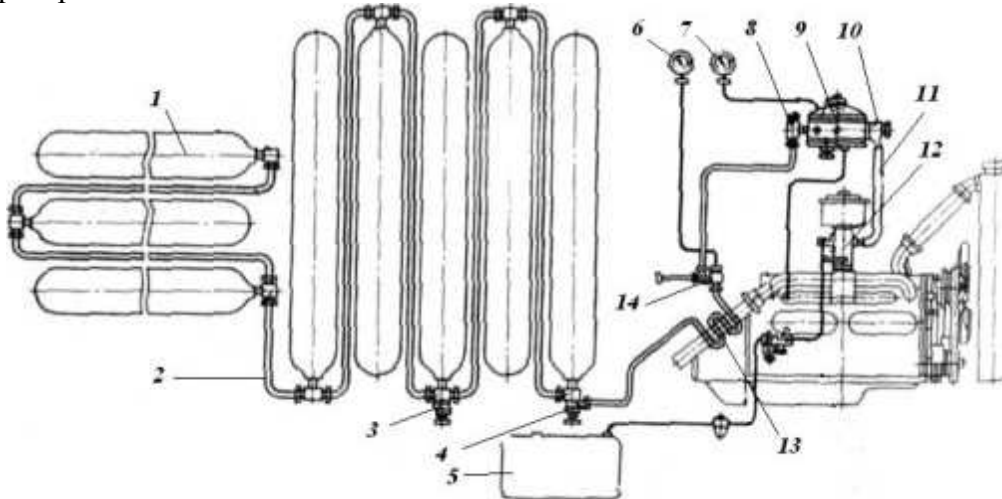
Схема газобаллонной установки для сжатого газа: 1 - баллон; 2 - газопровод высокого давления; 3 - наполнительный вентиль; 4 - расходный вентиль; 5 - топливный бак; 6 и 7 - манометры соответственно высокого и низкого давления; 8 - газовый фильтр; 9 - двухступенчатый газовый редуктор; 10 - дозирующее устройство газового редуктора; 11 - газопровод низкого давления; 12 - карбюратор-смеситель; 13 - подогреватель сжатого газа; 14 - магистральный вентиль
